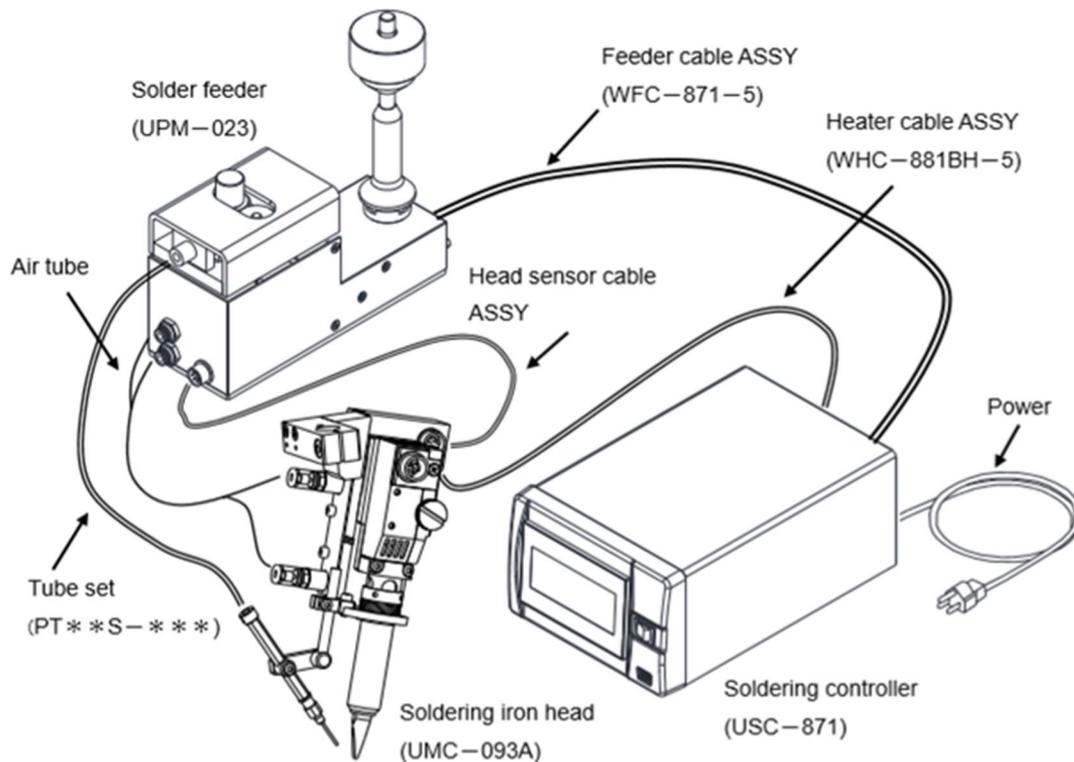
Esquema de la unidad de soldadura USP5 de Japan Unix. Cortesía de [7].
